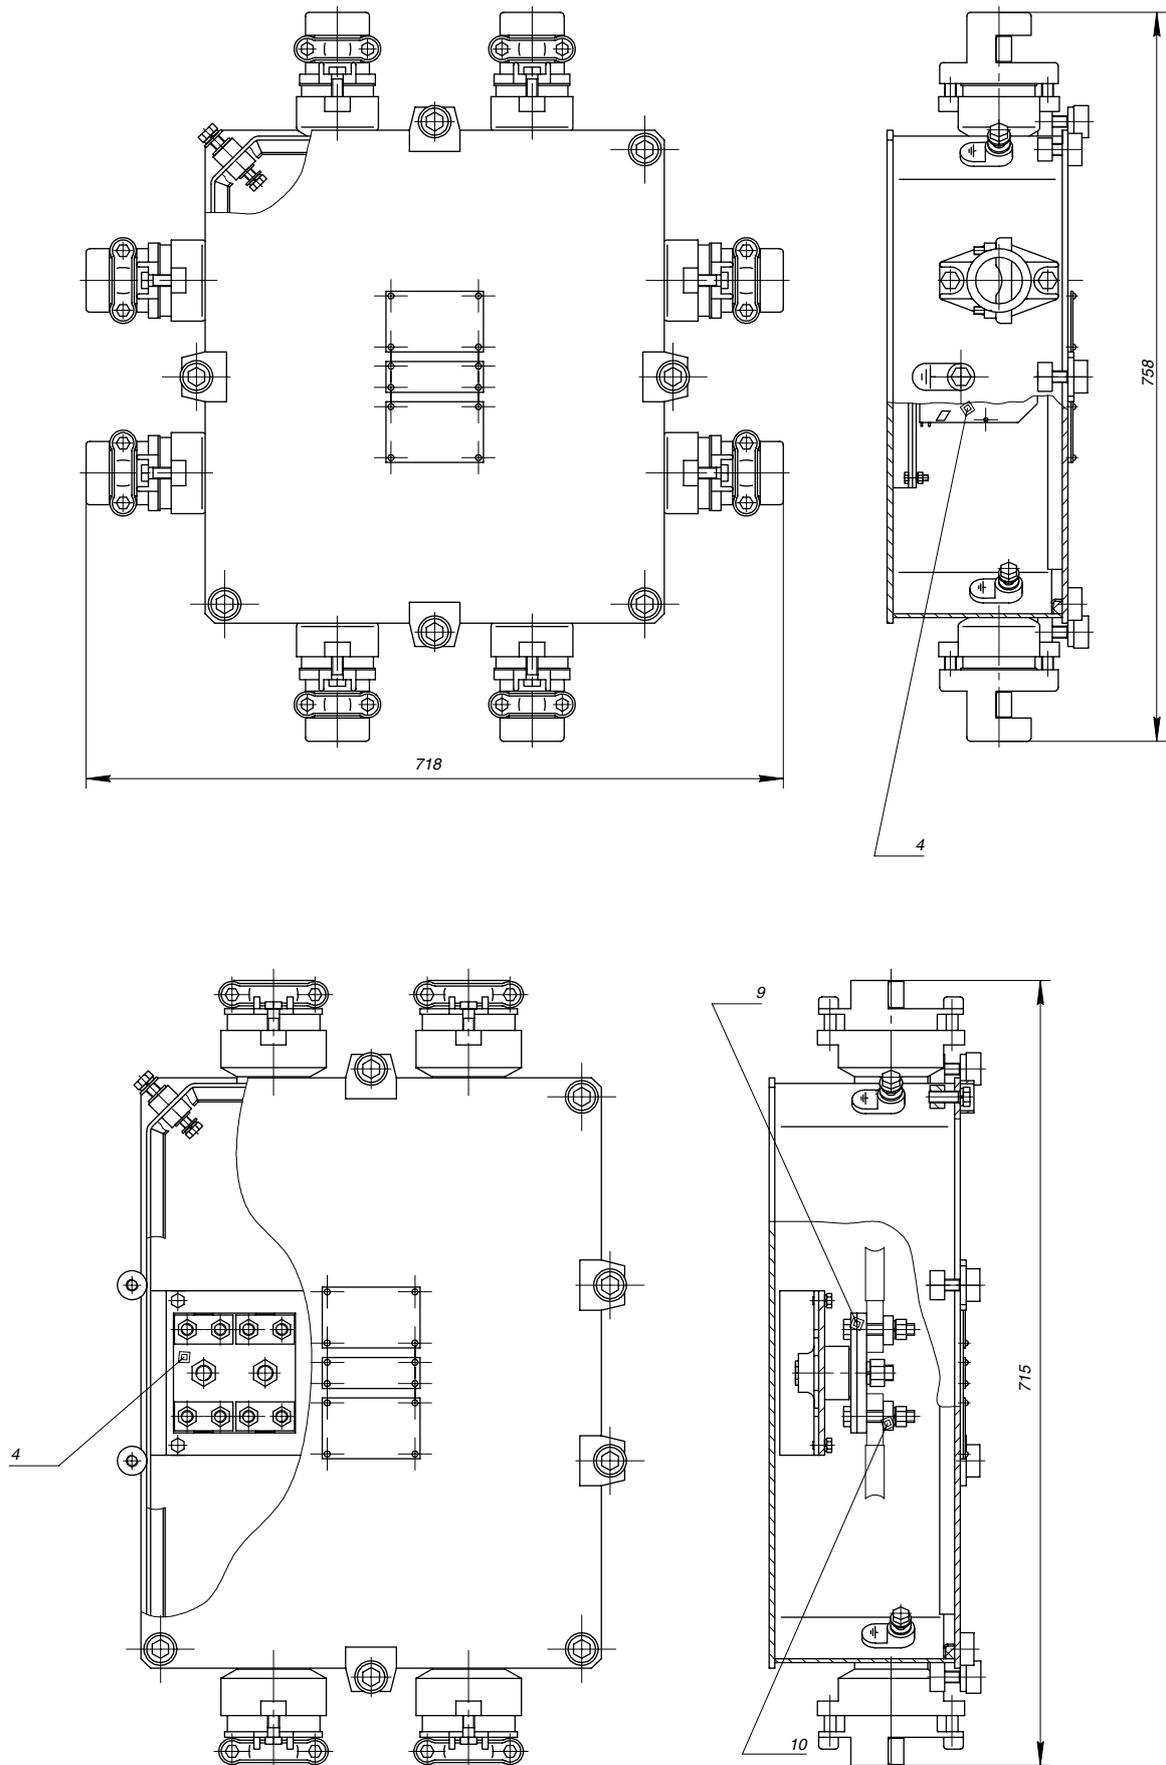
Общий вид и габаритные размеры (мм) устройств UCSH-5 и UCSH-6
